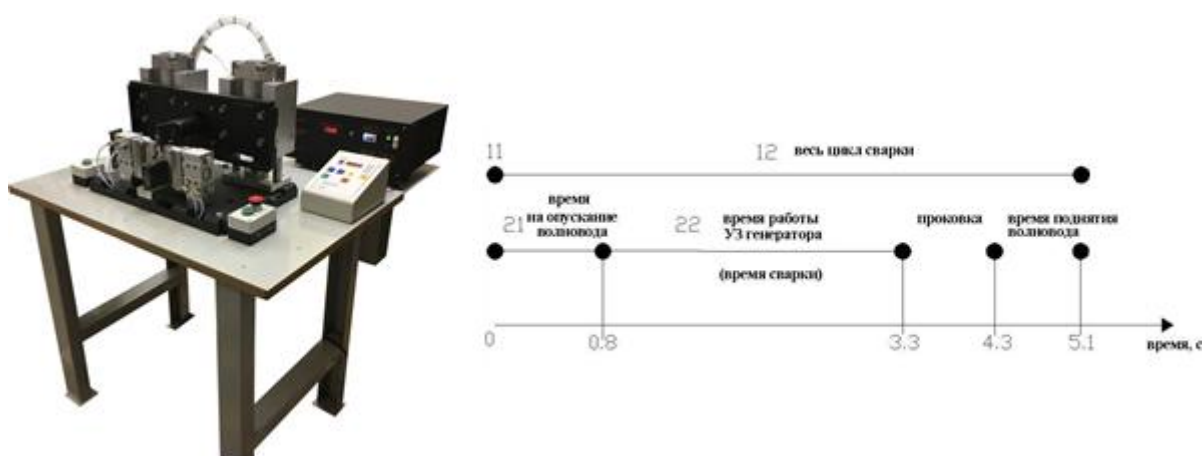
Ультразвуковая сварочная машина для сварки металлов и пример цикла ультразвуковой сварки металлических изделий
